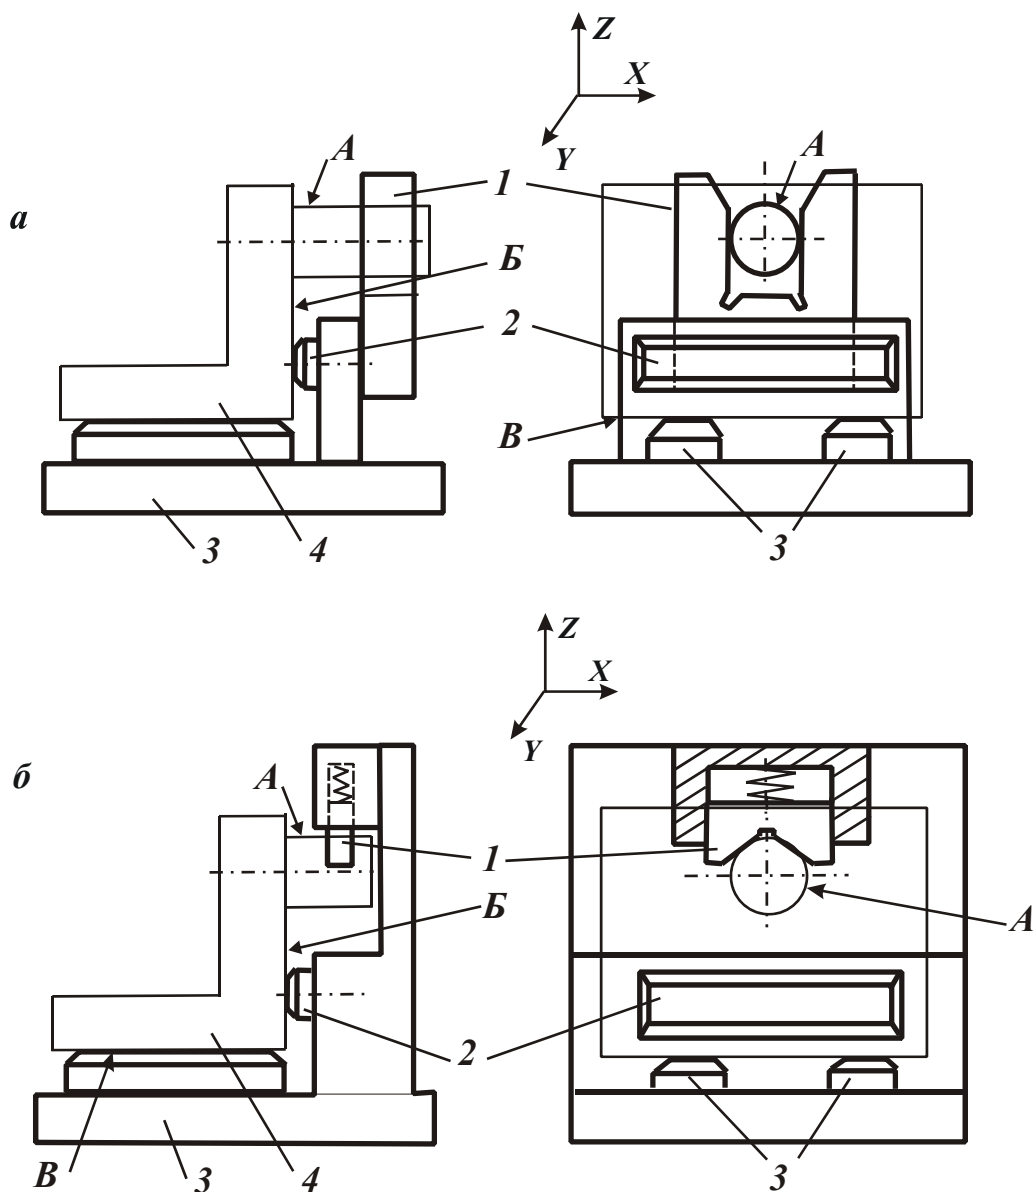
Способы базирования заготовки дополнительной базой в виде наружной цилиндрической поверхности, ось которой параллельна одной и перпендикулярна другой базе, уже получившей базирование.
